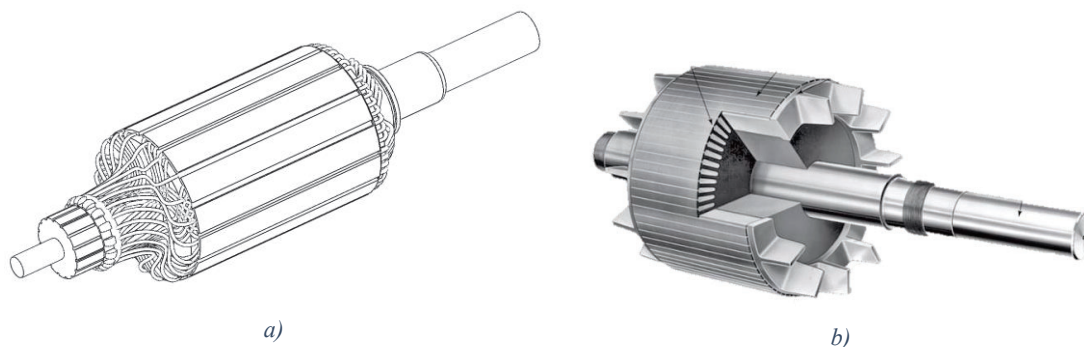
Tipos de rotor en máquinas síncronas. a) Rotor bobinado y b) Rotor jaula de ardilla. Fuente [14]
